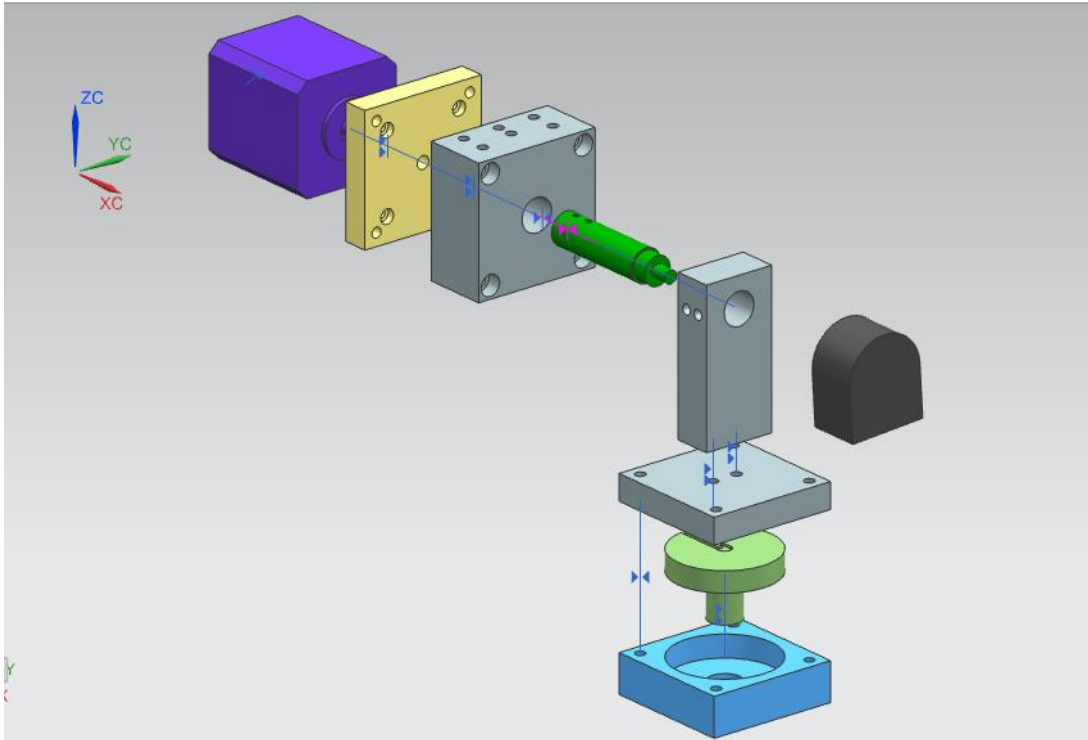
Diseño 3. Ensamble vista isométrica explosiva.
